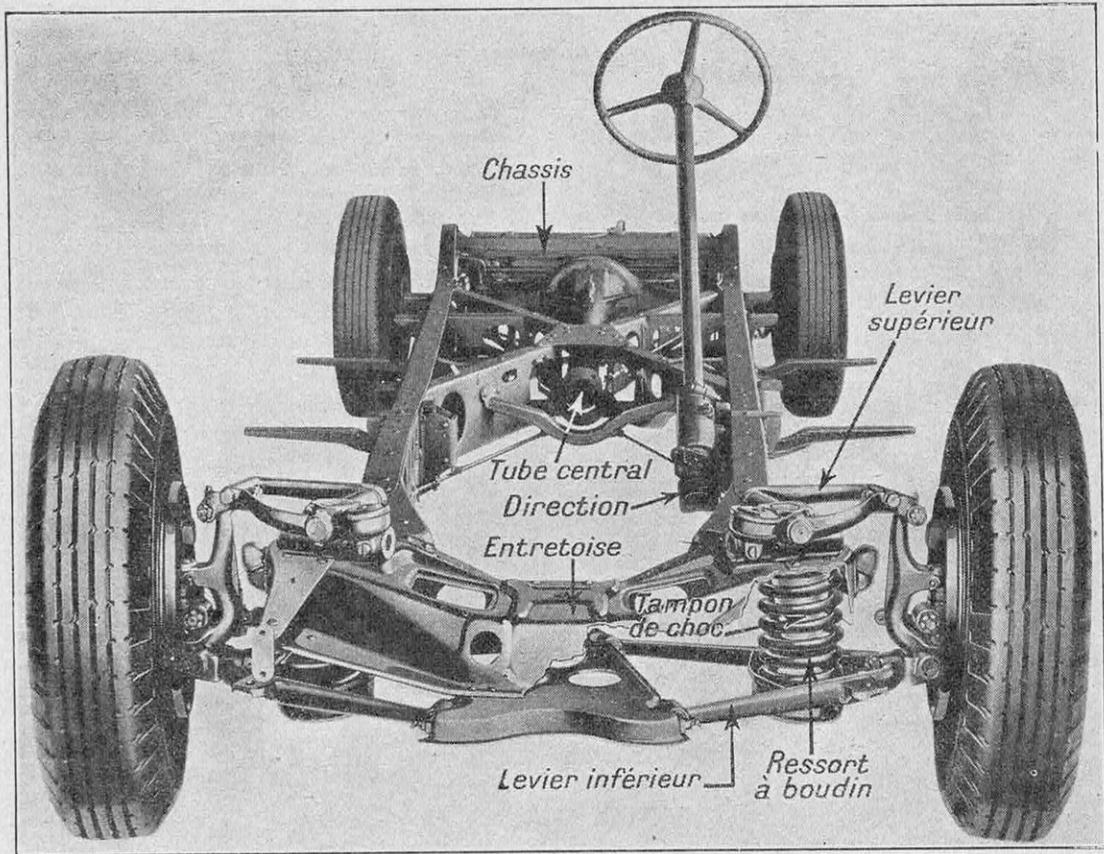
VUE GÉNÉRALE D'UN CHASSIS « BUICK » A CADRE RIGIDE ET ROUES AVANT INDÉPENDANTES PAR LEVIERS OSCILLANTS, RESSORTS A BOUDIN ET TAMPONS DE CHOC EN CAOUTCHOUC
